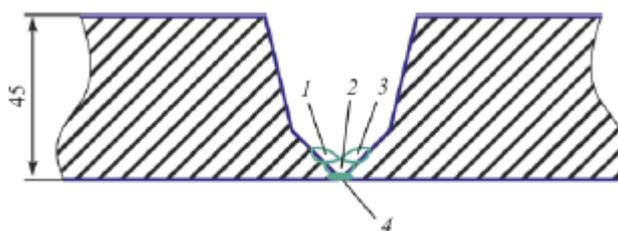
Проварка корня шва: 1-4 – порядок наложения валиков
